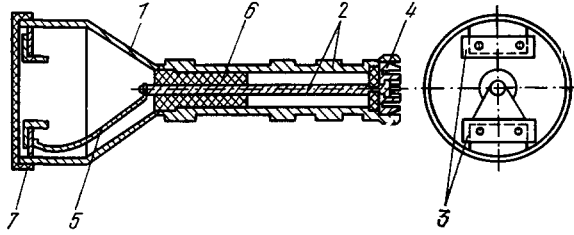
Схематическое изображение конструкции рупорного излучателя.
